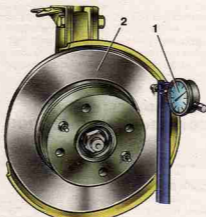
Проверка осевого биения тормозного диска: 1 – индикатор; 2 – тормозной диск
